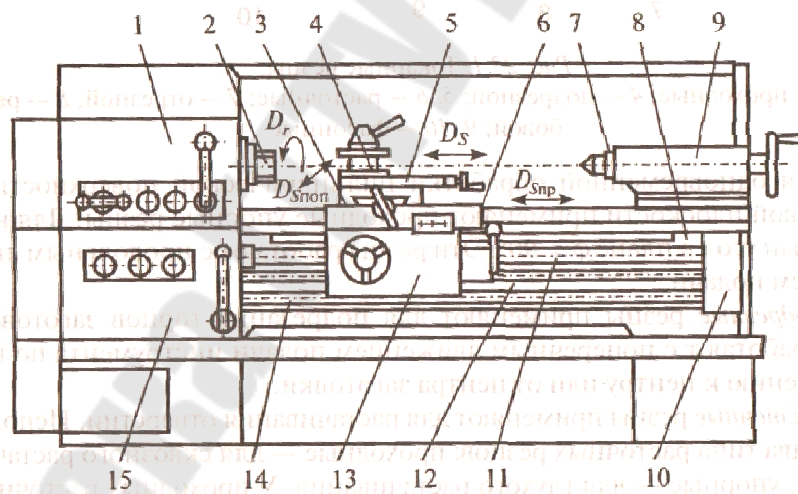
Общий вид токарно-винторезного станка 16К20
